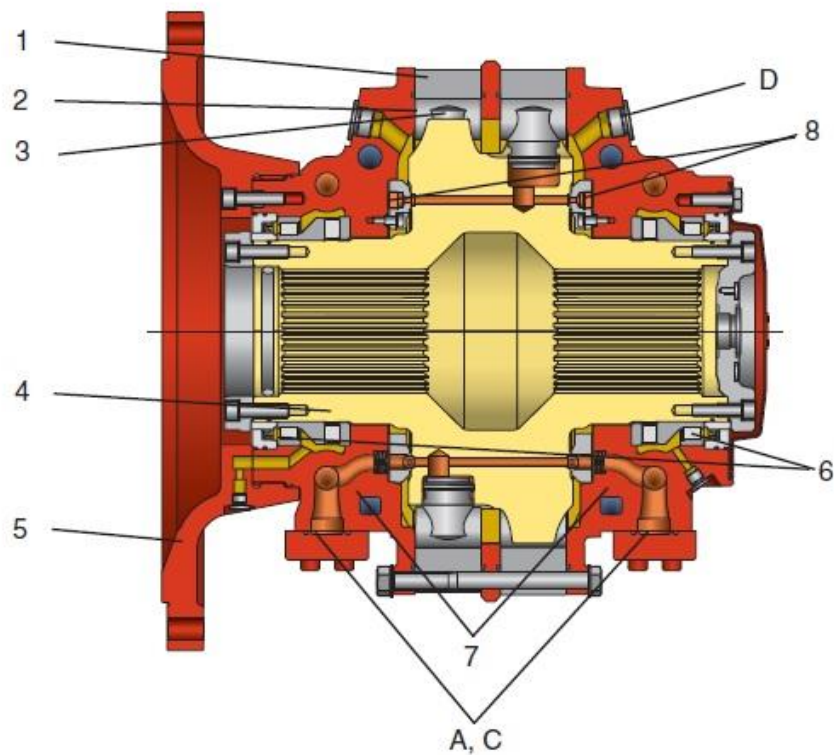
hydromotor Compact CB EN 734-7h – [24, obr. ze str. 6]
